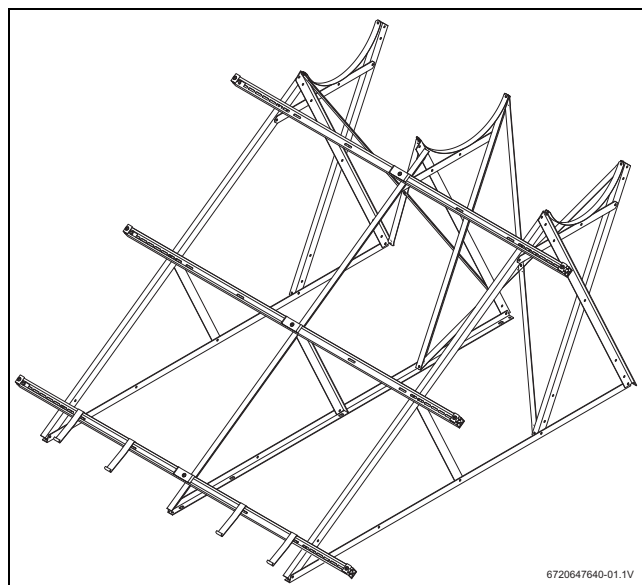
Vista de conjunto del soporte para cubierta plana (sistema de 300 l)
